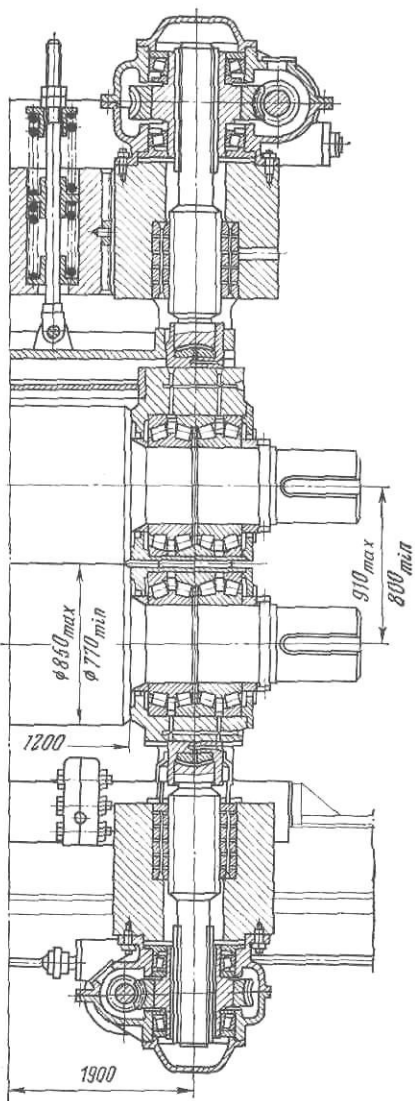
Рабочая клеть 850×1200 мм непрерывного заготовочного стана $850/700/500$
